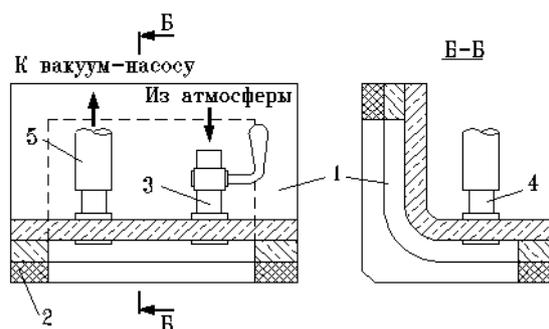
Вакуумная камера угловая для испытания герметичности сварных швов: 1 – корпус из оргстекла; 2 – губчатая резина; 3 – кран; 4 – патрубок; 5 – шланг
